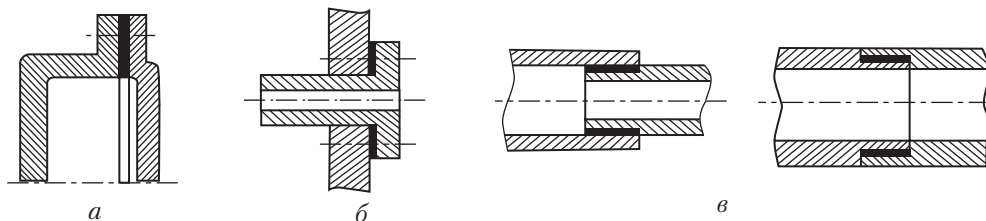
Розрізи з'єднань тверднучою замазкою:
